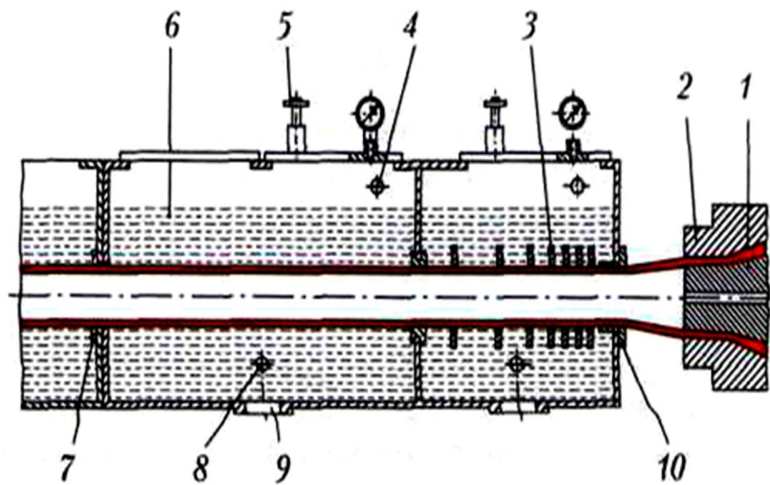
Зовнішнє калібрування труби за допомогою вакууму: 1- дорн; 2- форсунка; 3- калібруючі кільця; 4 - вакуум-з'єднання; 5- гвинт; 6- охолоджуюча ванна; 7- ущільнення; 8 - подача води; 9 - калібруюча втулка; 10 - стік води.
